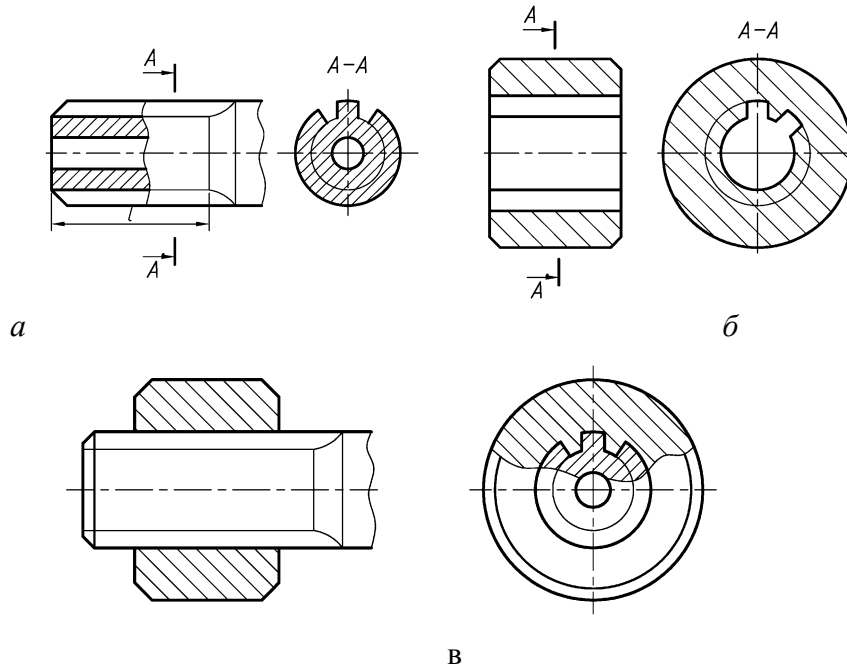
Изображение шлицевых деталей с прямоугольным профилем зуба:
